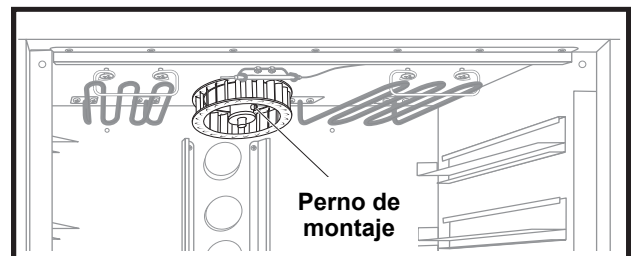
Perno de montaje de la rueda del ventilador del horno.
